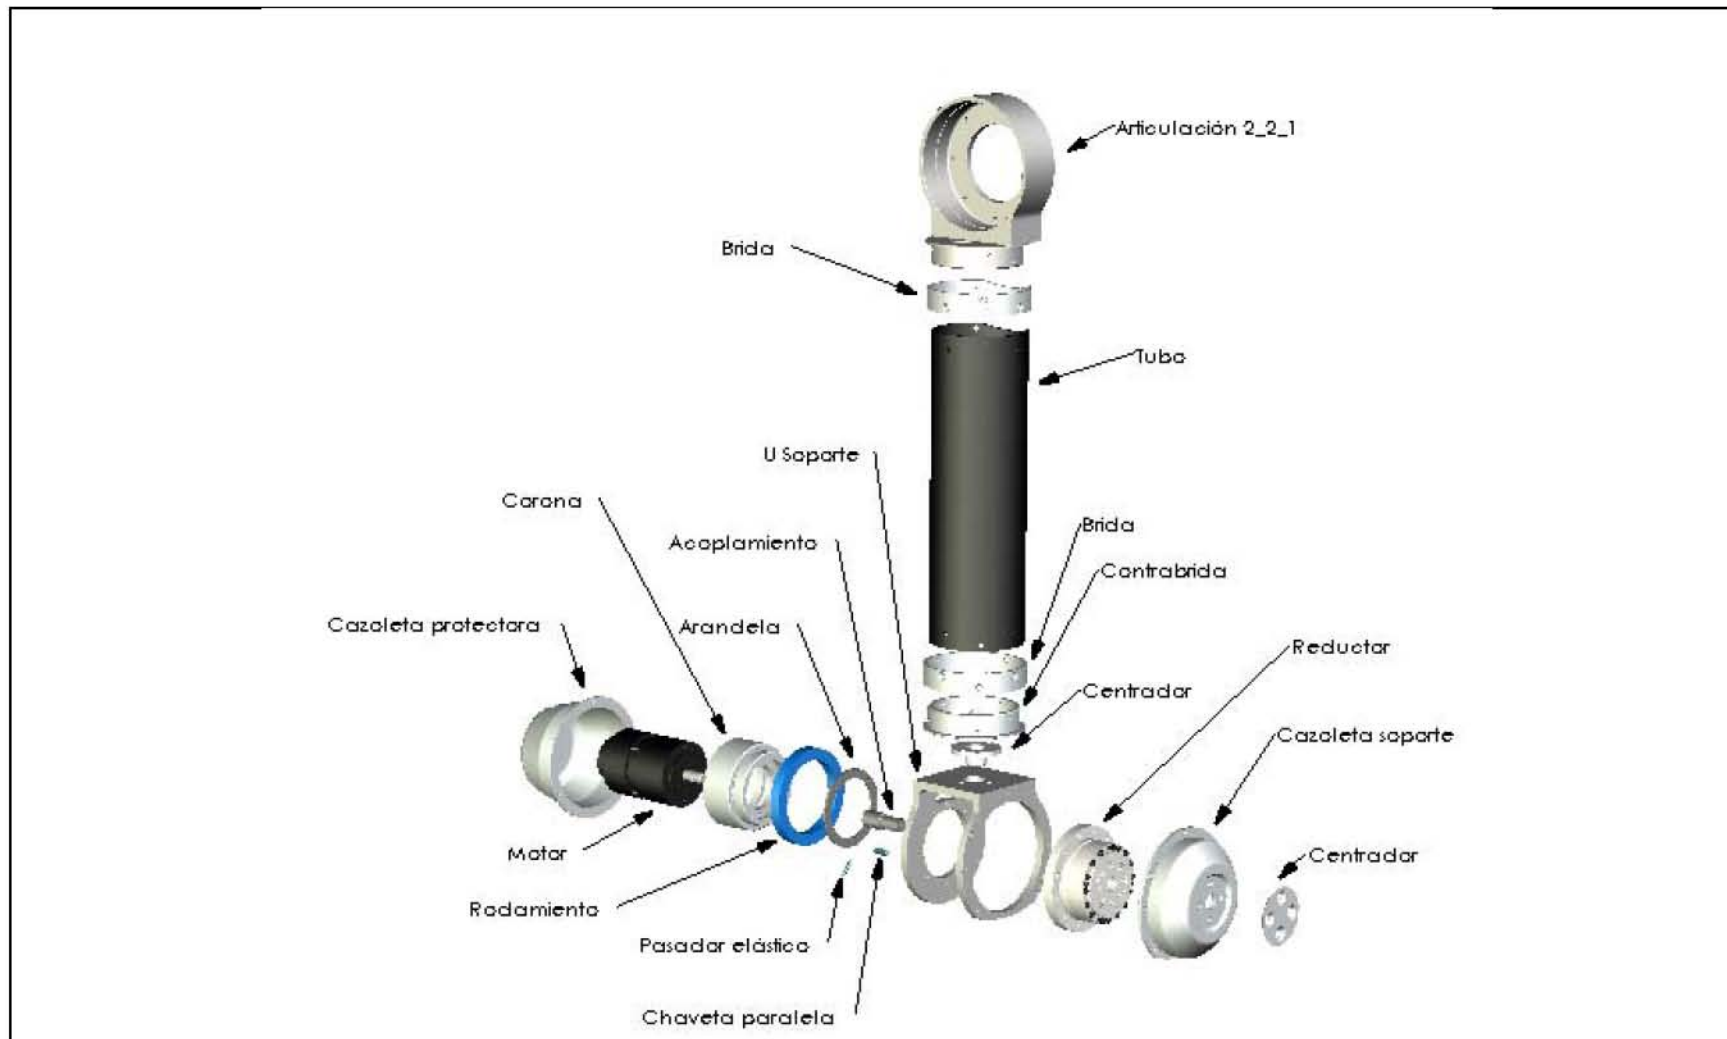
Vista explosionada del sub-ensamblaje 1.
